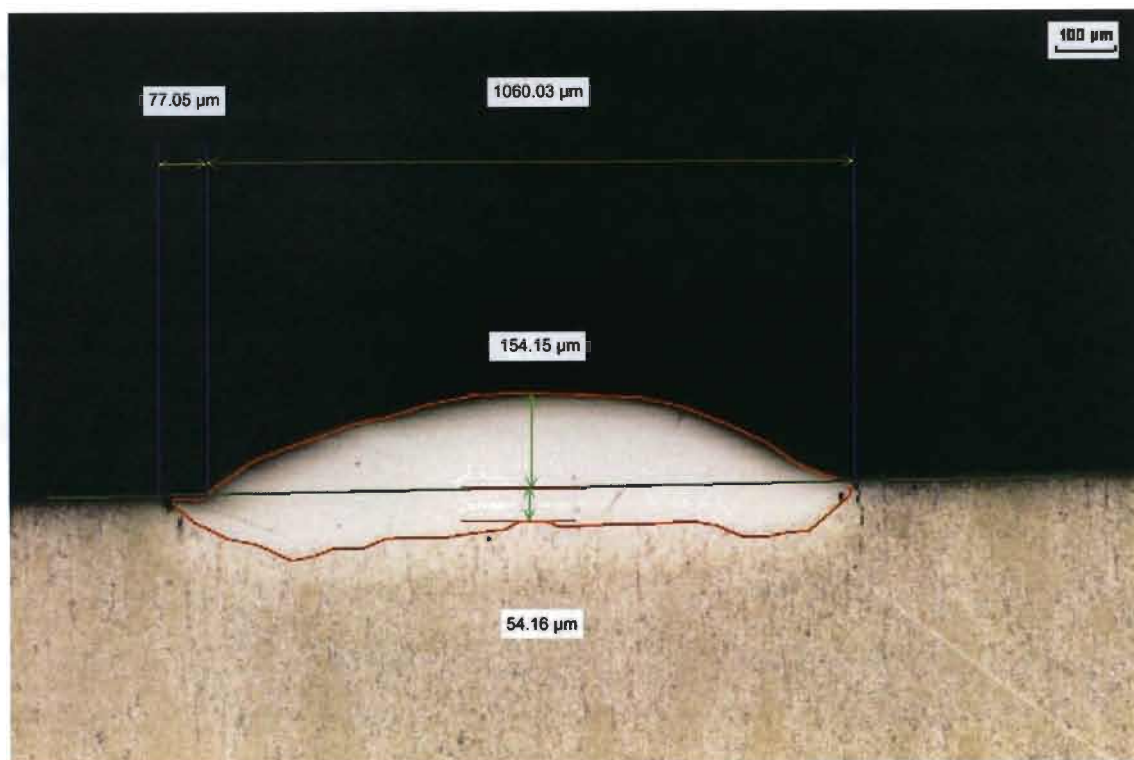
7 Cordón de soldadura 3 visto a 5X
